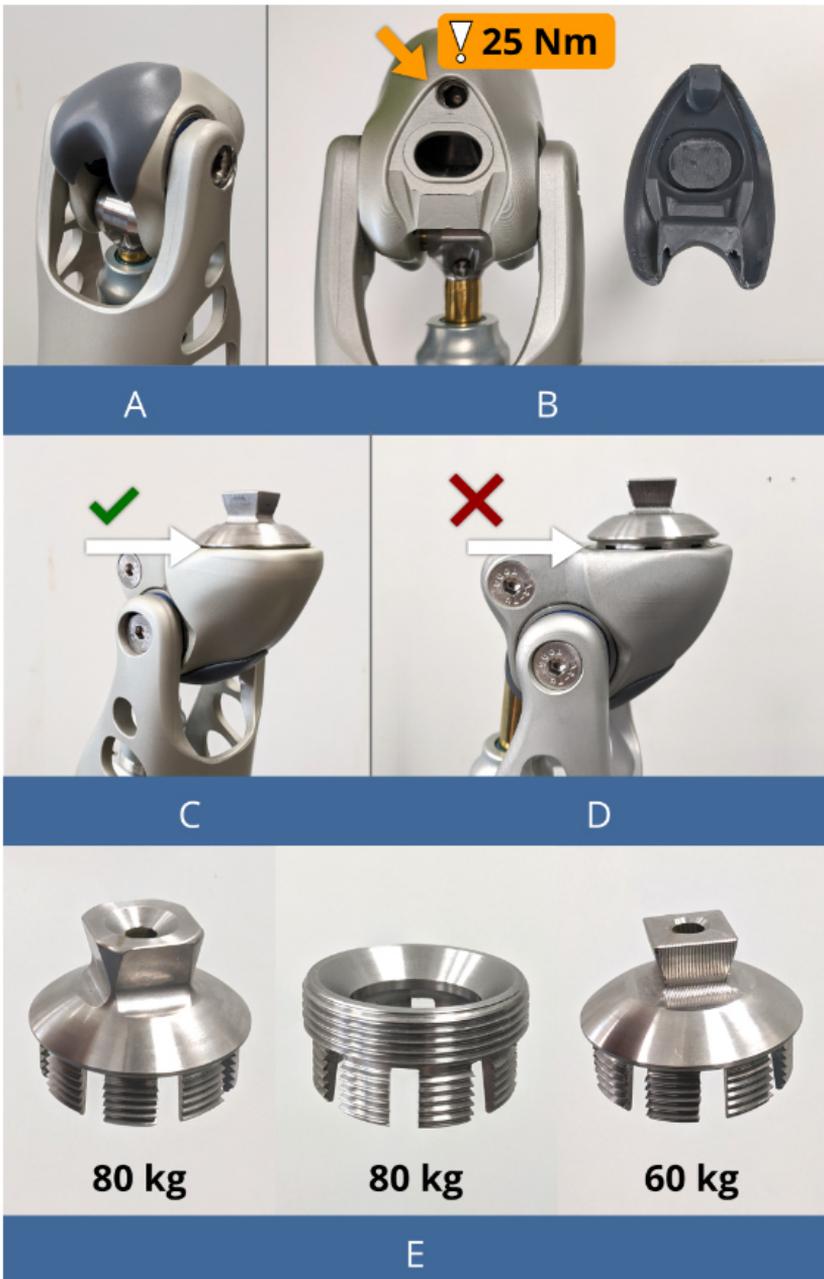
(A) Die Kniekappe wird entfernt, wenn das Knie vollständig gebeugt ist, so dass sie von der Rückseite ausgehängt werden kann. (B) Beim Entfernen der Kniekappe wird eine Schraube sichtbar, die mit einem 5 mm Sechskant gesichert wird. (C) Der proximale Adapter wird so auf die Oberseite des VGK-X/VGK-XS geschraubt, dass der Spalt weniger als einen mm beträgt. (D) Der Spalt zwischen proximalen Adapter und VGK darf nicht mehr als einen mm betragen. (E) Die wählbaren Proximaladapter für das 80 kg und das 60 kg System.
